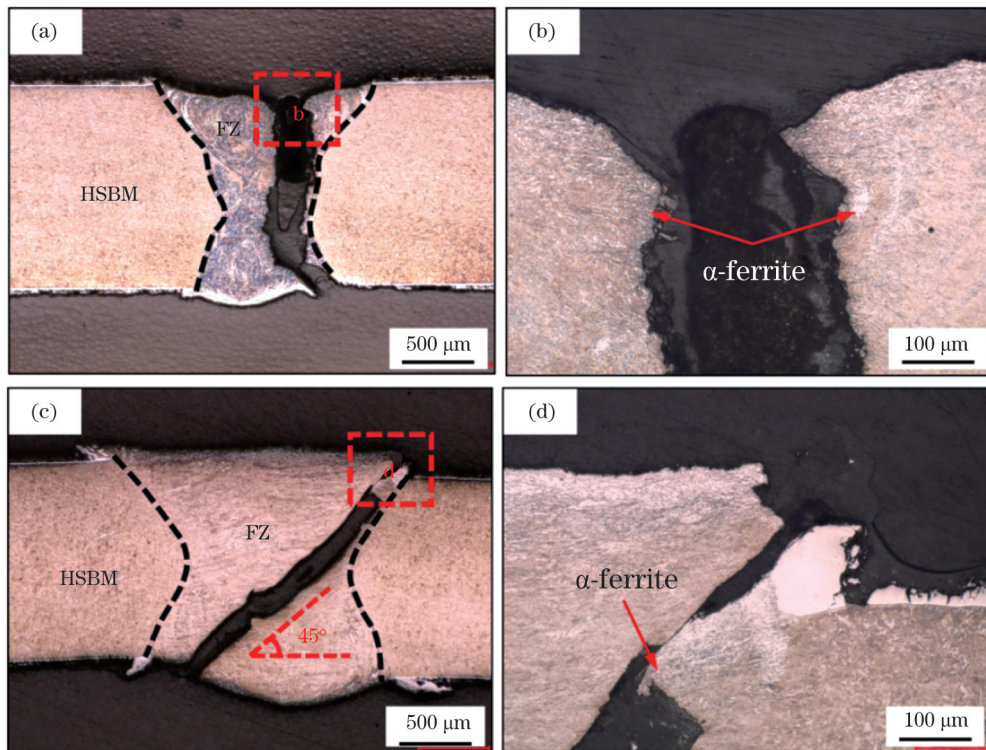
热冲压后焊接接头的断裂位置。(a)(b)LW 焊接接头;(c)(d)OLFW2 焊接接头
